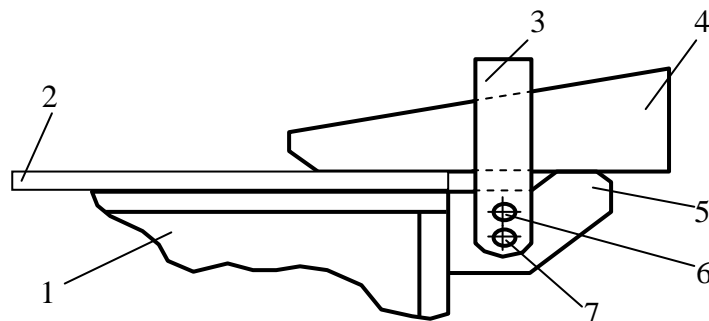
Клиновий притискач з відкидною скобою: 1-стенд; 2-заготовка; 3-скоба; 4-клин; 5-опорна планка; 6-штир; 7-вісь.
